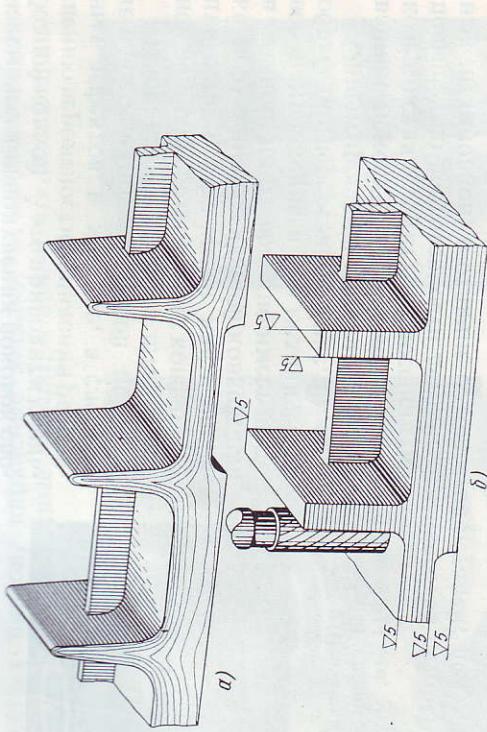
Схема расположения волокон в штампованных поковках (a) и обрабатываемых резанием деталях из катаных и кованых заготовок (б)
